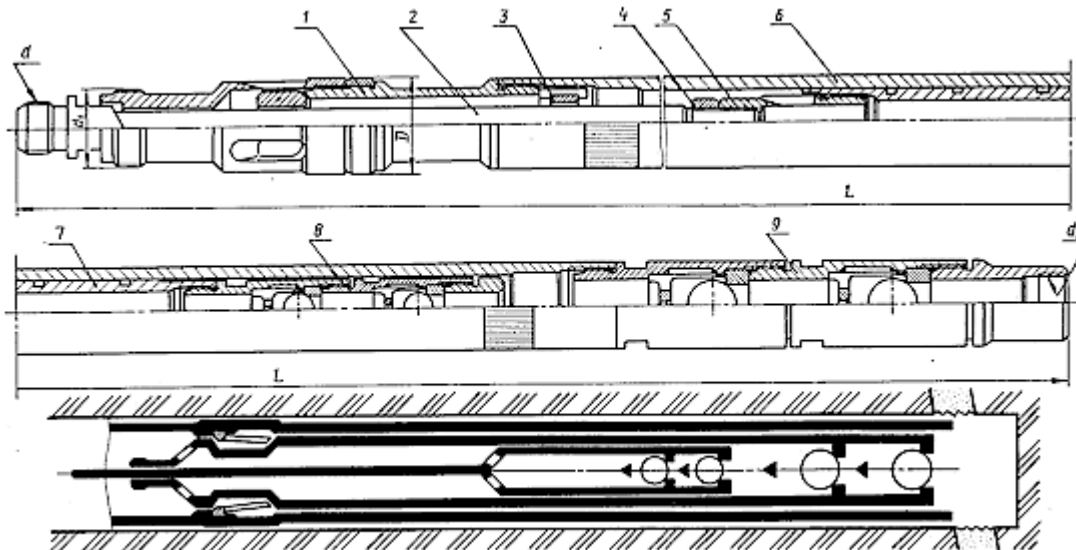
ШГН: 1 - замок; 2 - шток; 3 - упор; 4 - контргайка; 5 - клетка плунжера; 6 - цилиндр; 7 - плунжер; 8 - нагнетательный клапан; 9 - всасывающий клапан
